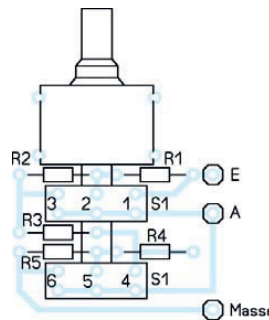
Leiterführung und Bestückung für einen Miniaturdreheschalter mit zwei Schaltkammern; beide Kammern fungieren als eine Schalterebene, da sie um 90° versetzt gegeneinander auf die Welle geschoben sind und ihre Kontakte somit bei Betätigung des Rastkopfes nacheinander schließen.
